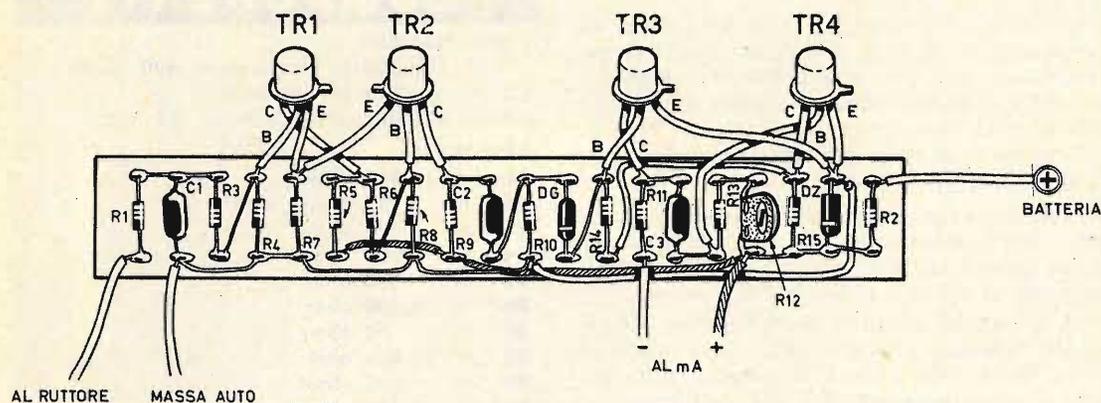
Utilizzando componenti elettronici miniaturizzati, il piano di cablaggio dei contagiri elettronico può essere realizzato su una basetta di materiale isolante di piccole dimensioni. Tutte le resistenze, fatta eccezione per R2, sono da 1/4 di watt.
